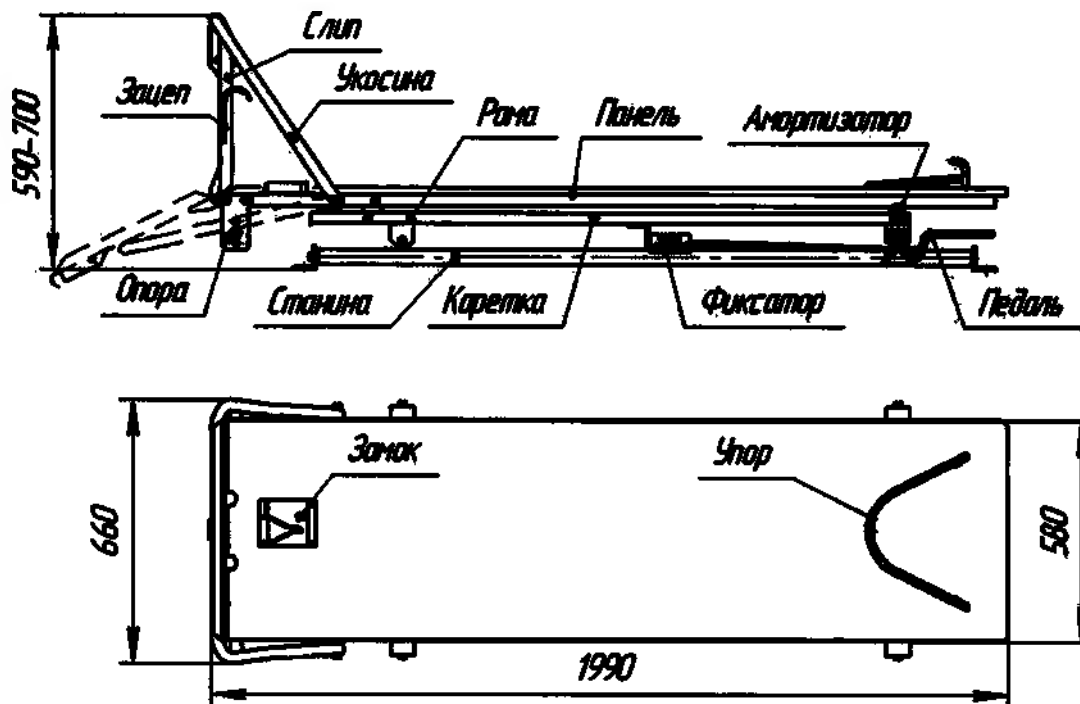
Устройство приемное с поперечным перемещением УП-ММ (общий вид).
